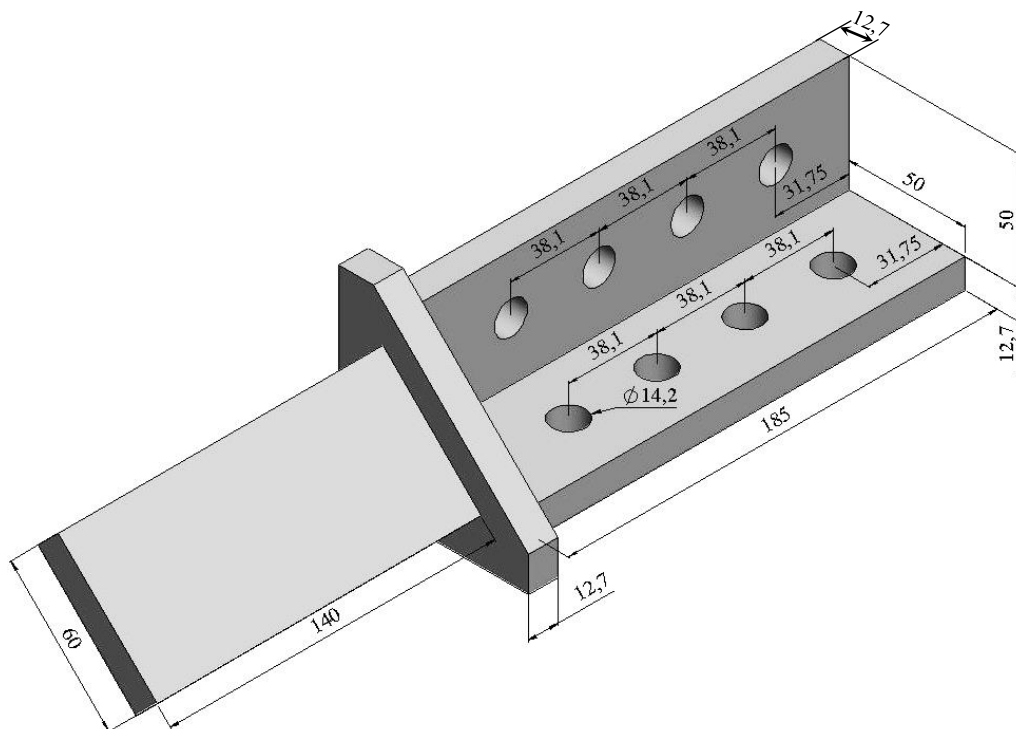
Dispositivo com 12,7 mm de espessura para fixação de cantoneiras 50x50 mm em todas as abas conectadas, dimensões em (mm)
